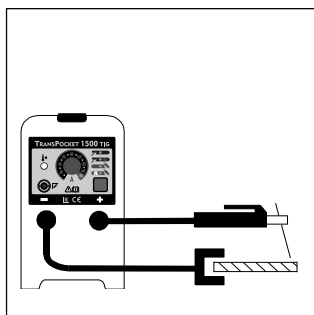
TP 1500 equipado para soldadura com eléctrodos de barra
